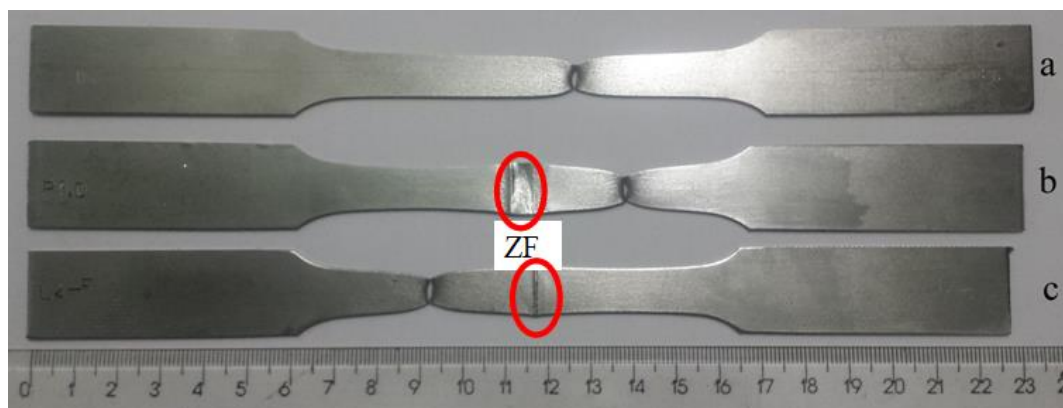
Corpos de prova fraturados após ensaio de tração. a) Metal base; b) Junta soldada a plasma; c) Junta soldada a laser.
